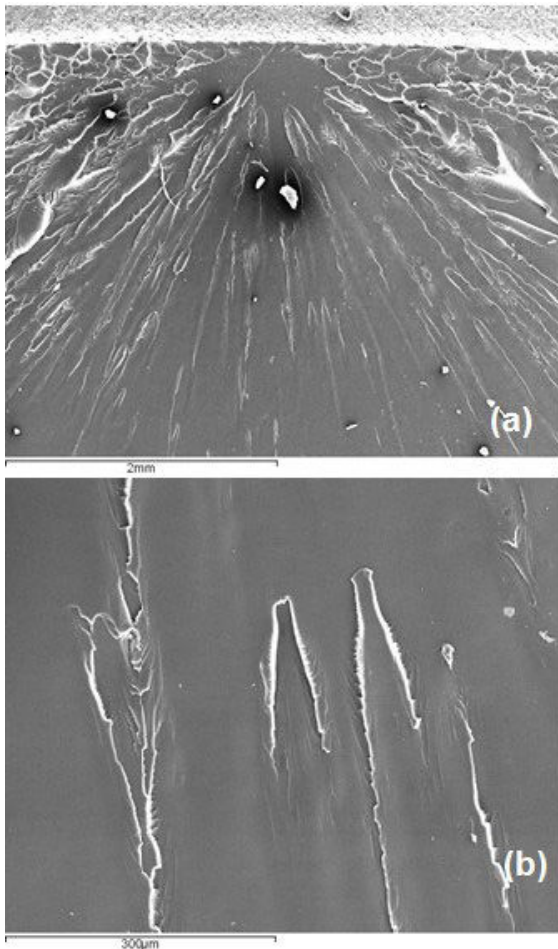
Superfície de fractura de um provete sem cortiça. (a) – Visão geral da fractura. (b) – Detalhe da superfície de fractura.
